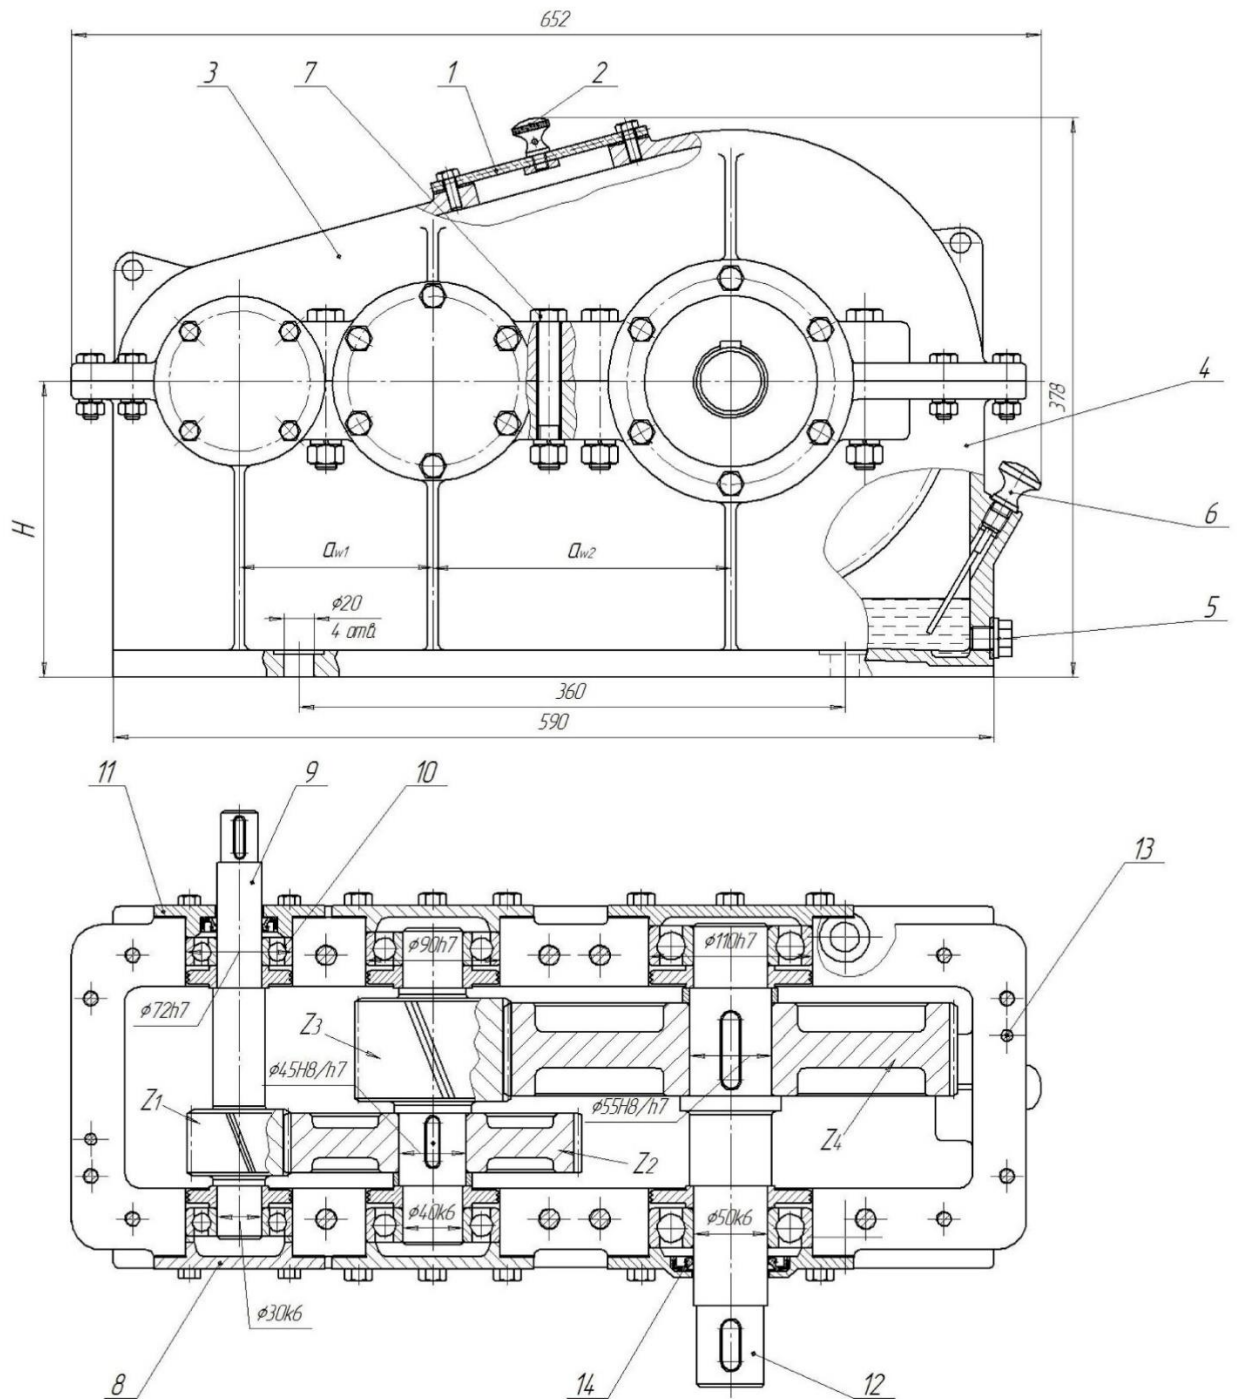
Редуктор циліндричний двохступінчастий
